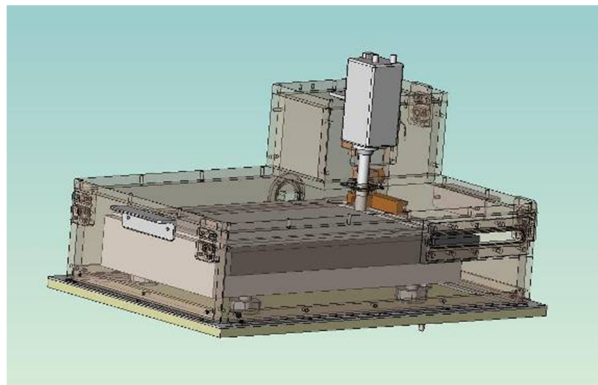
Конструкционный чертеж разработанного защитного колпака.
